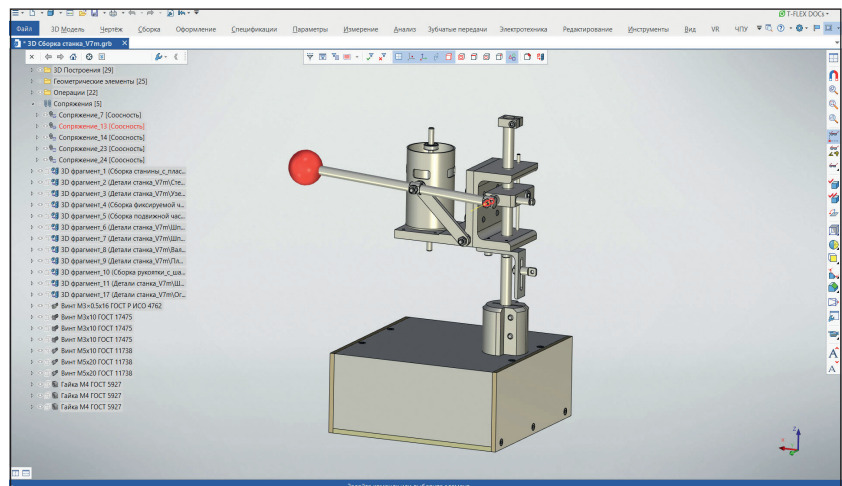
3D-модель сверлильного станка для радиолюбителей
